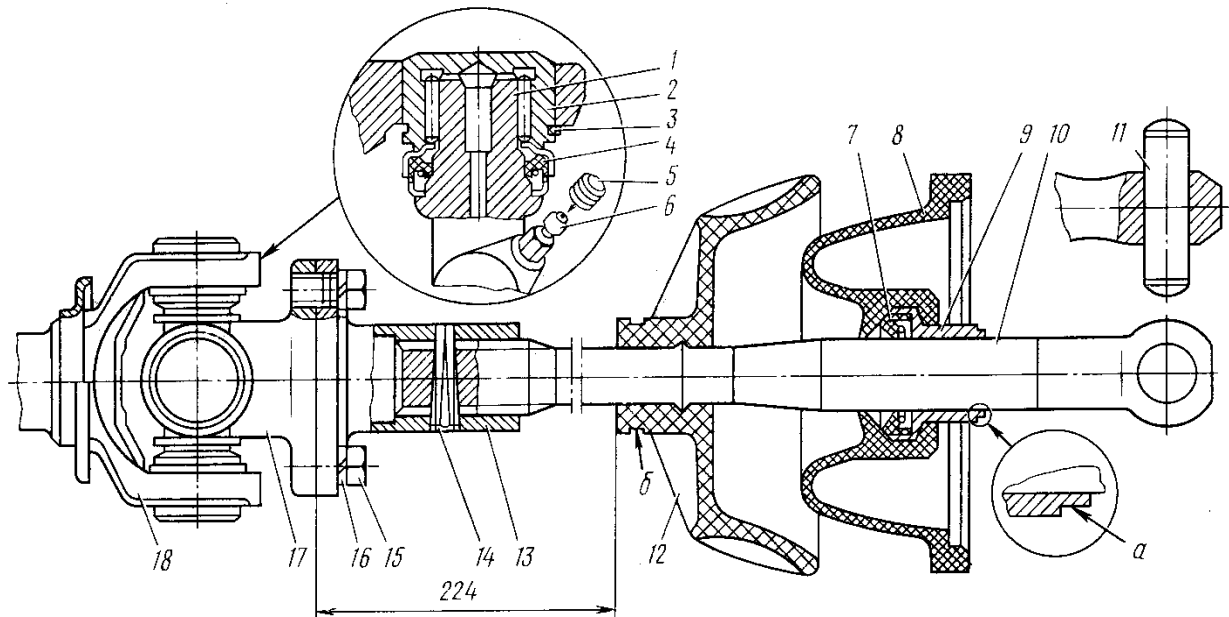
Полуось в сборе: 1 — крестовина, 2 — подшипник, 3 — стопорное кольцо; 4, 7 — манжеты; 5 — колпачок; 6 — пресс-масленка; 8 — защитный чехол; 9 — корпус манжеты; 10 — полуось; 11 — палец; 12 — грязеотражатель; 13 — фланец; 14 — штифт; 15 — болт; 16 — шайба; 17 — ведущая вилка; 18 — ведомая вилка;
